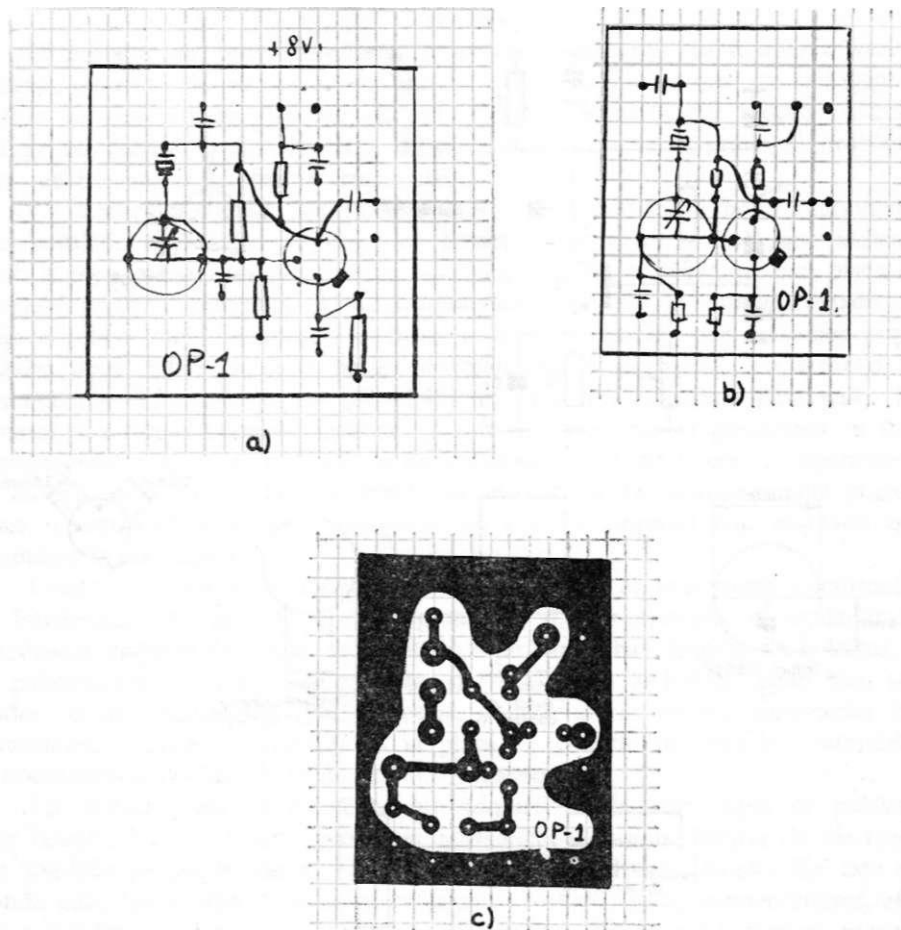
Diseño del circuito impreso: A) dibujo del oscilador de portadora; B) dibujo reducido; C) dibujo del circuito impreso del oscilador de portadora.
